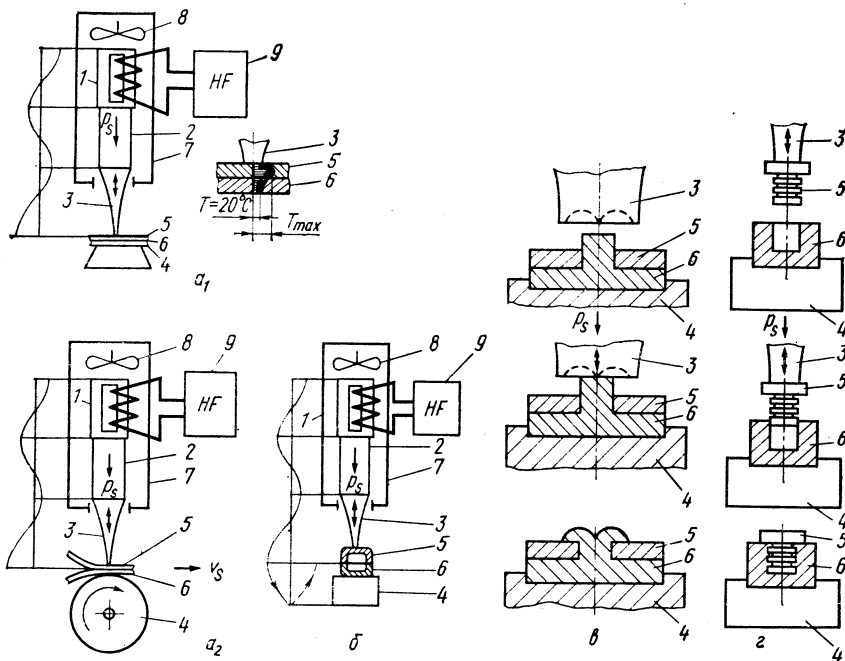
Принцип ультразвуковой сварки:
